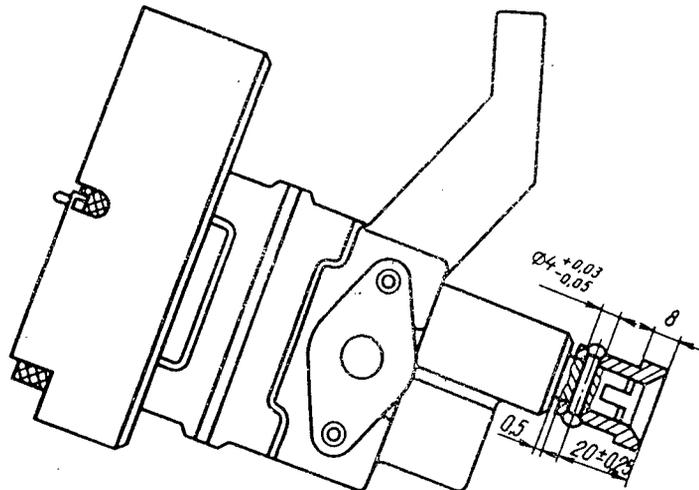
Befestigung der Büchse auf der Ölpumpenwelle
